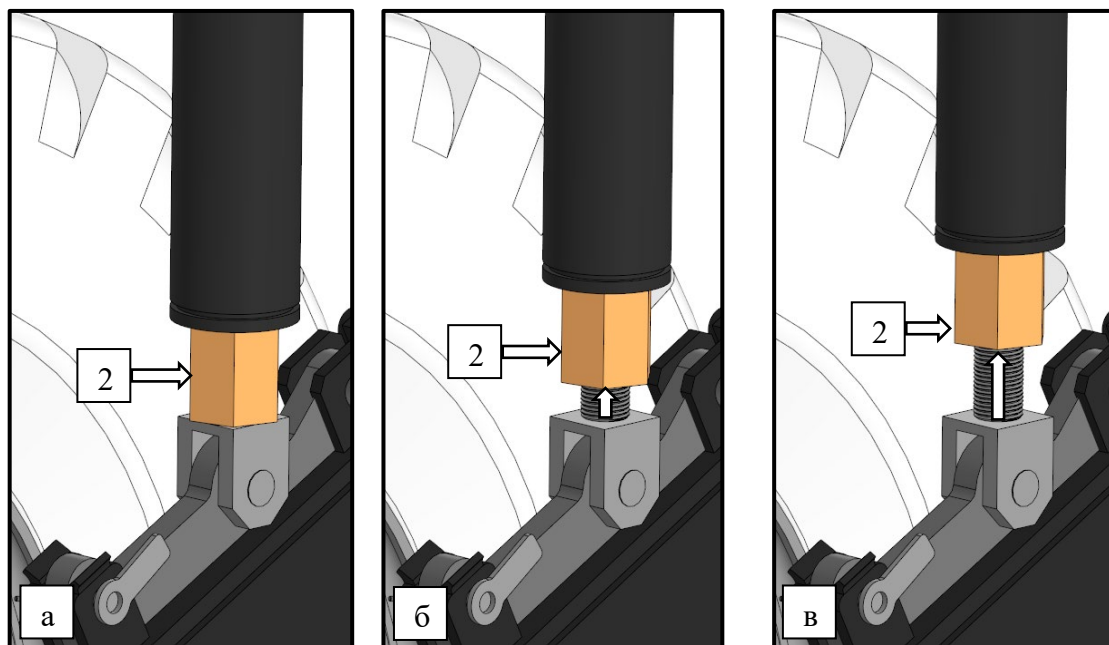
Регулировка упорной гайки на гидроцилиндрах:
